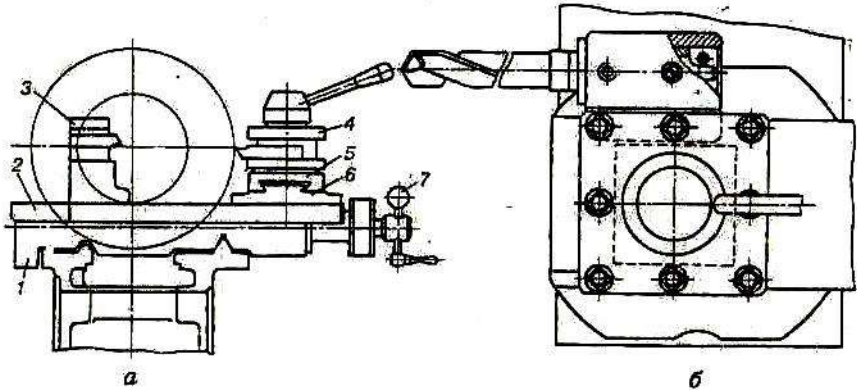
Схема супорта верстата 16K20 (а) і тримача центрового інструменту (б)
